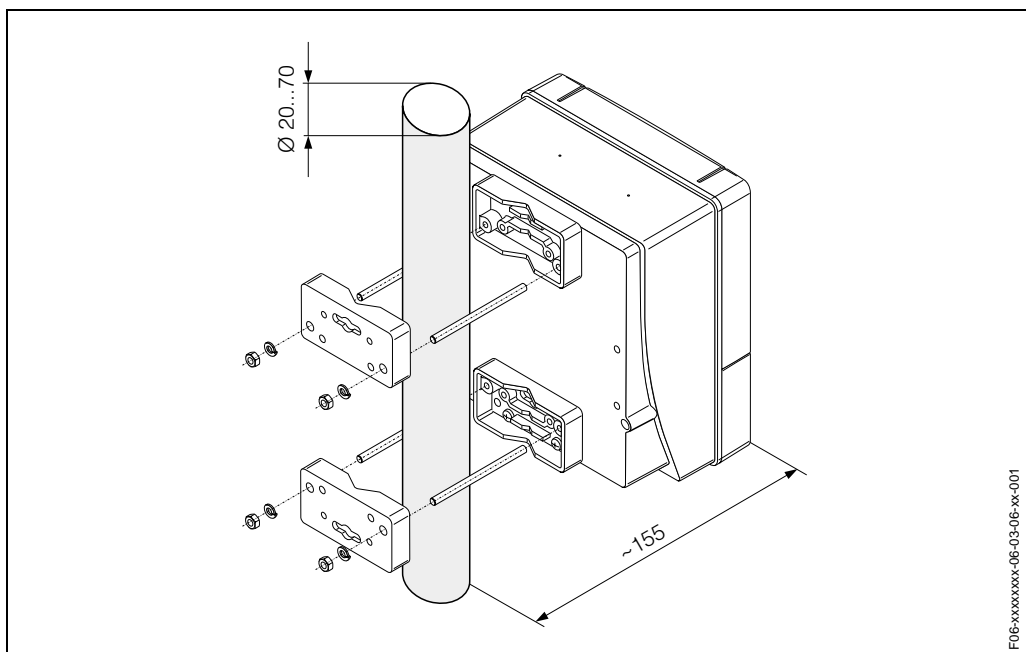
Montaje adosado a una tubería (caja para montaje pared)
